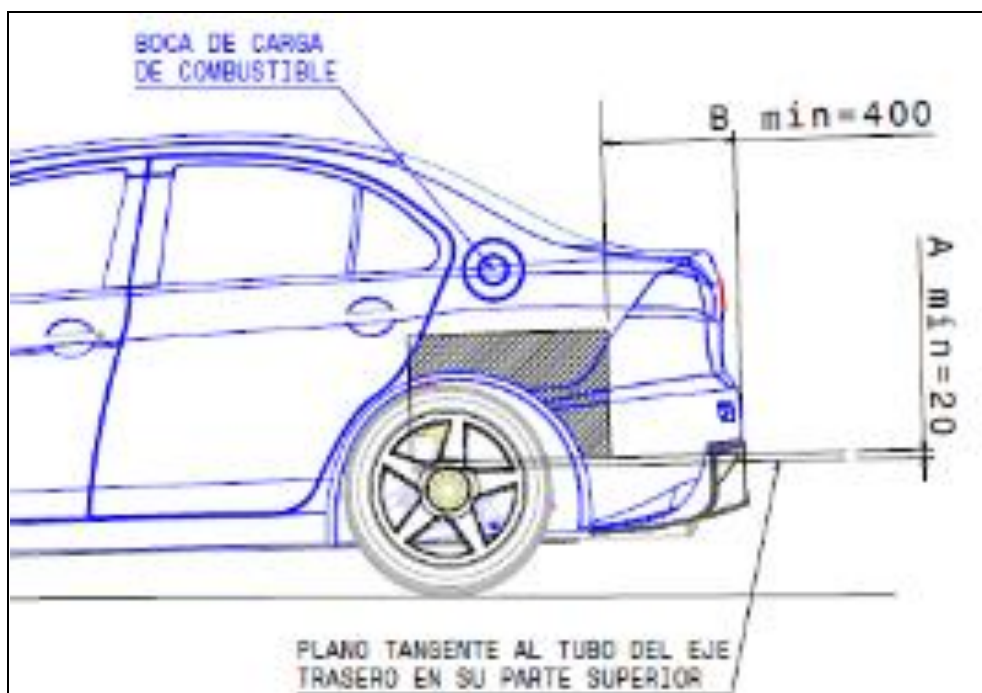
Posicionamiento del tanque de combustible y boca de recarga externa.
